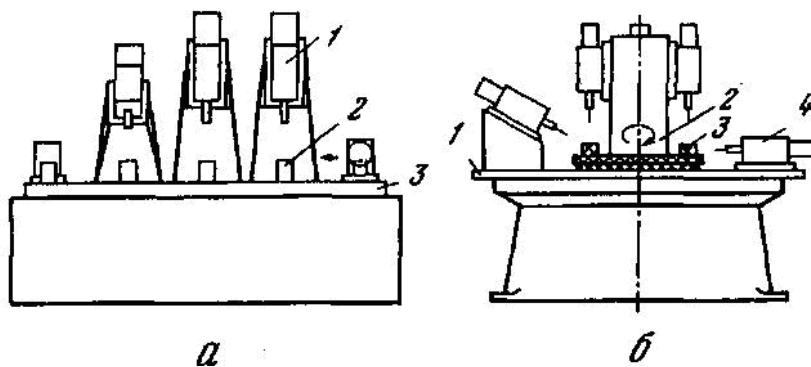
Компоновка агрегатних верстатів з прямолінійним переміщенням заготовок (а) і з центральною колоною (б)
